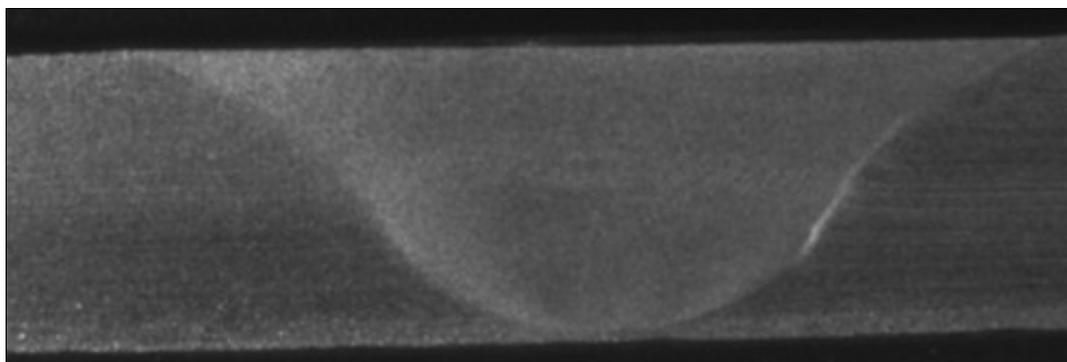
coupe métallographique de la soudure FSW sur de l'acier
